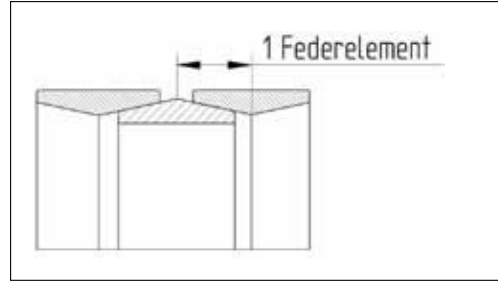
Zeichnung 2 Außenringe und 1 Innenring
